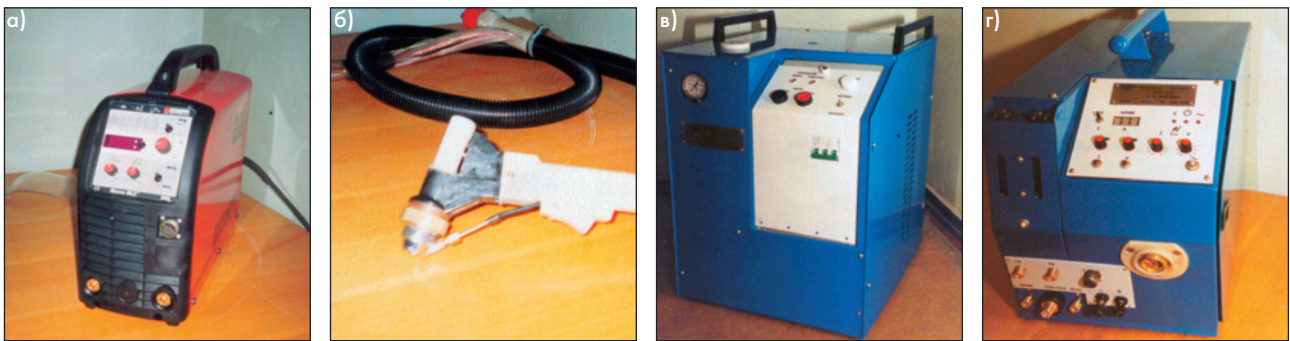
Модули полуавтомата: а — инверторный источник «Master 2500»; б — плазматрон; в — насосная станция охлаждения плазматрона; г — модуль управления с механизмом подачи сварочной проволоки
